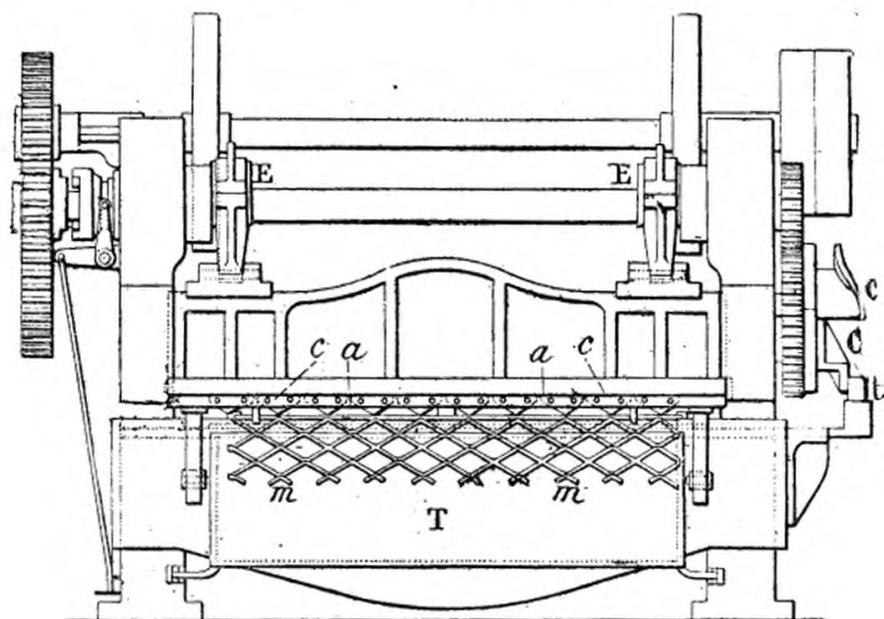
Elévation de la machine. — Vue d'arrière.
